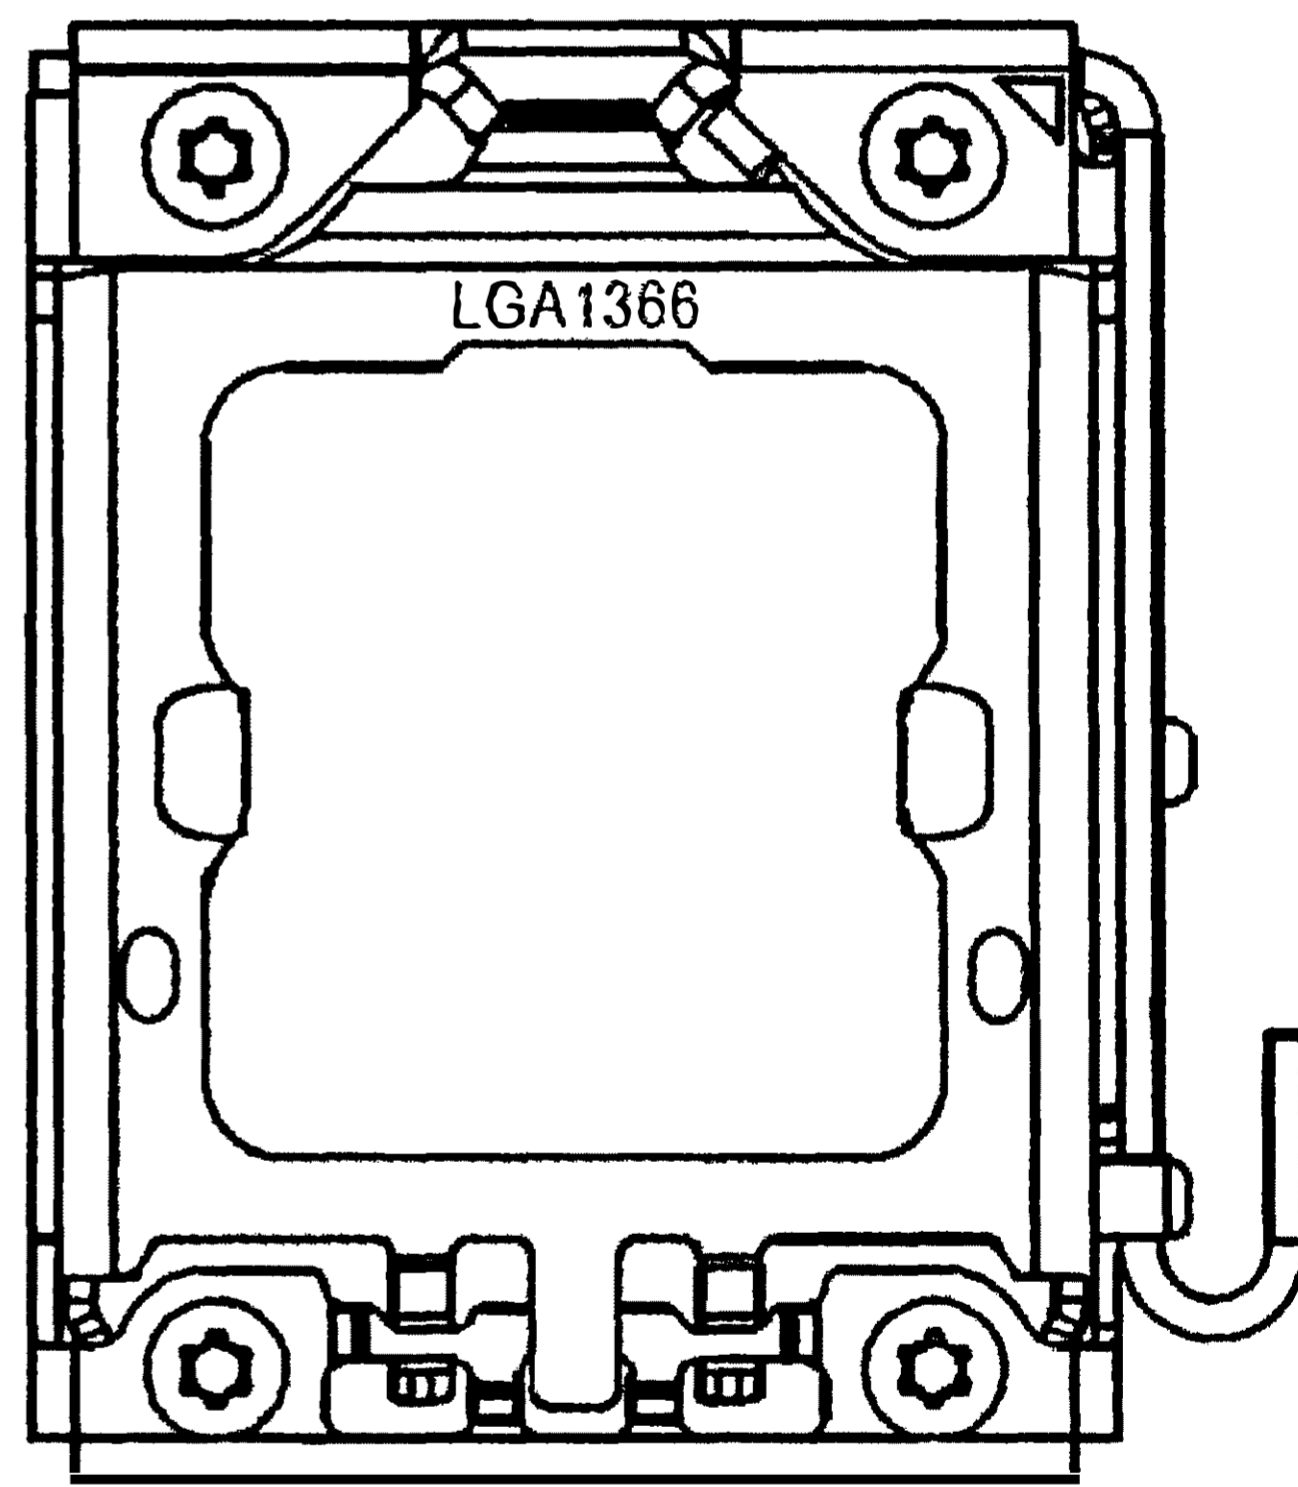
Гнездо Socket LGA1366 (Socket B)
